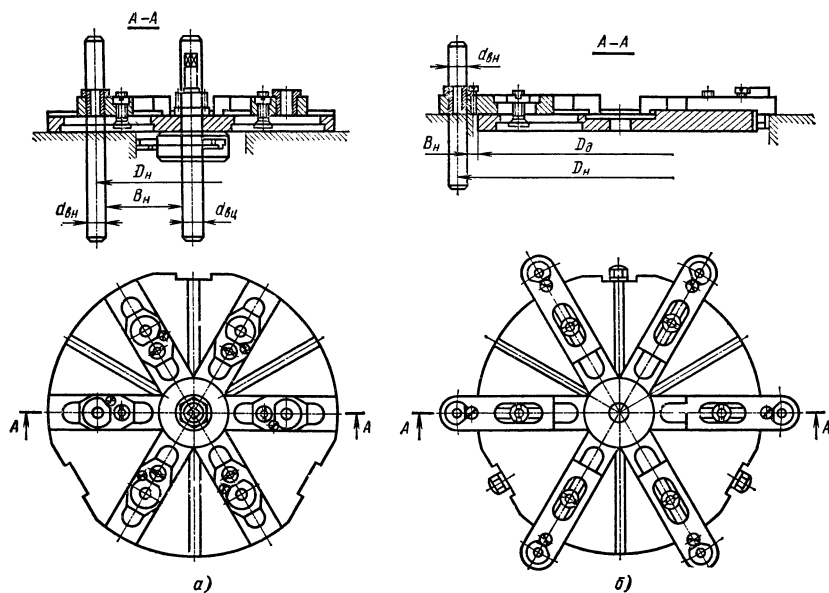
Накладные круглые кондукторы для сверления шести отверстий:
